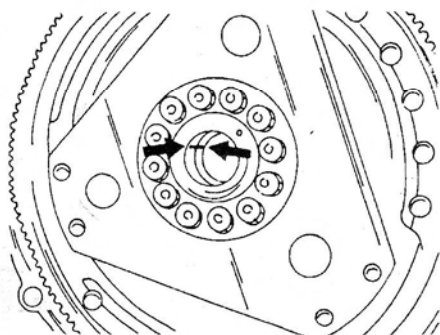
Маркировка положения приводного диска относительно коленчатого вала.
